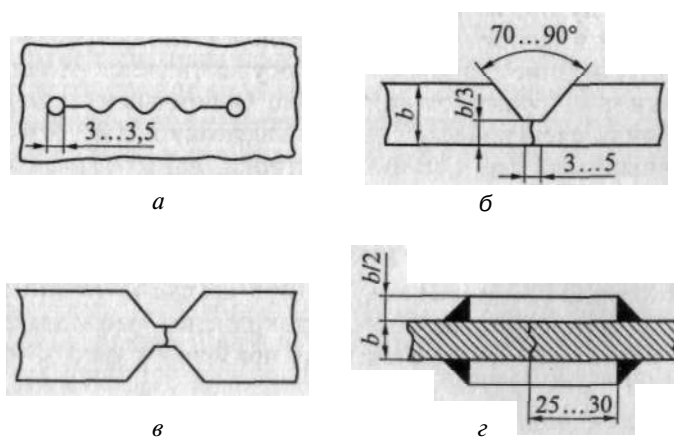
Схема подготовки деталей для заварки трещины:
